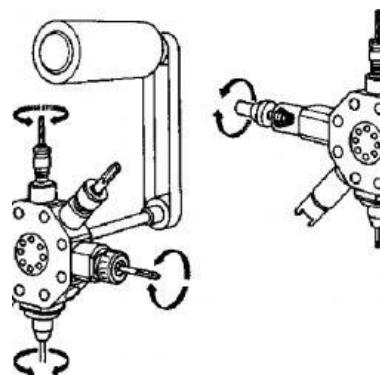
Конструктивная схема револьверной головки с вращающимися шпинделем токарного станка
